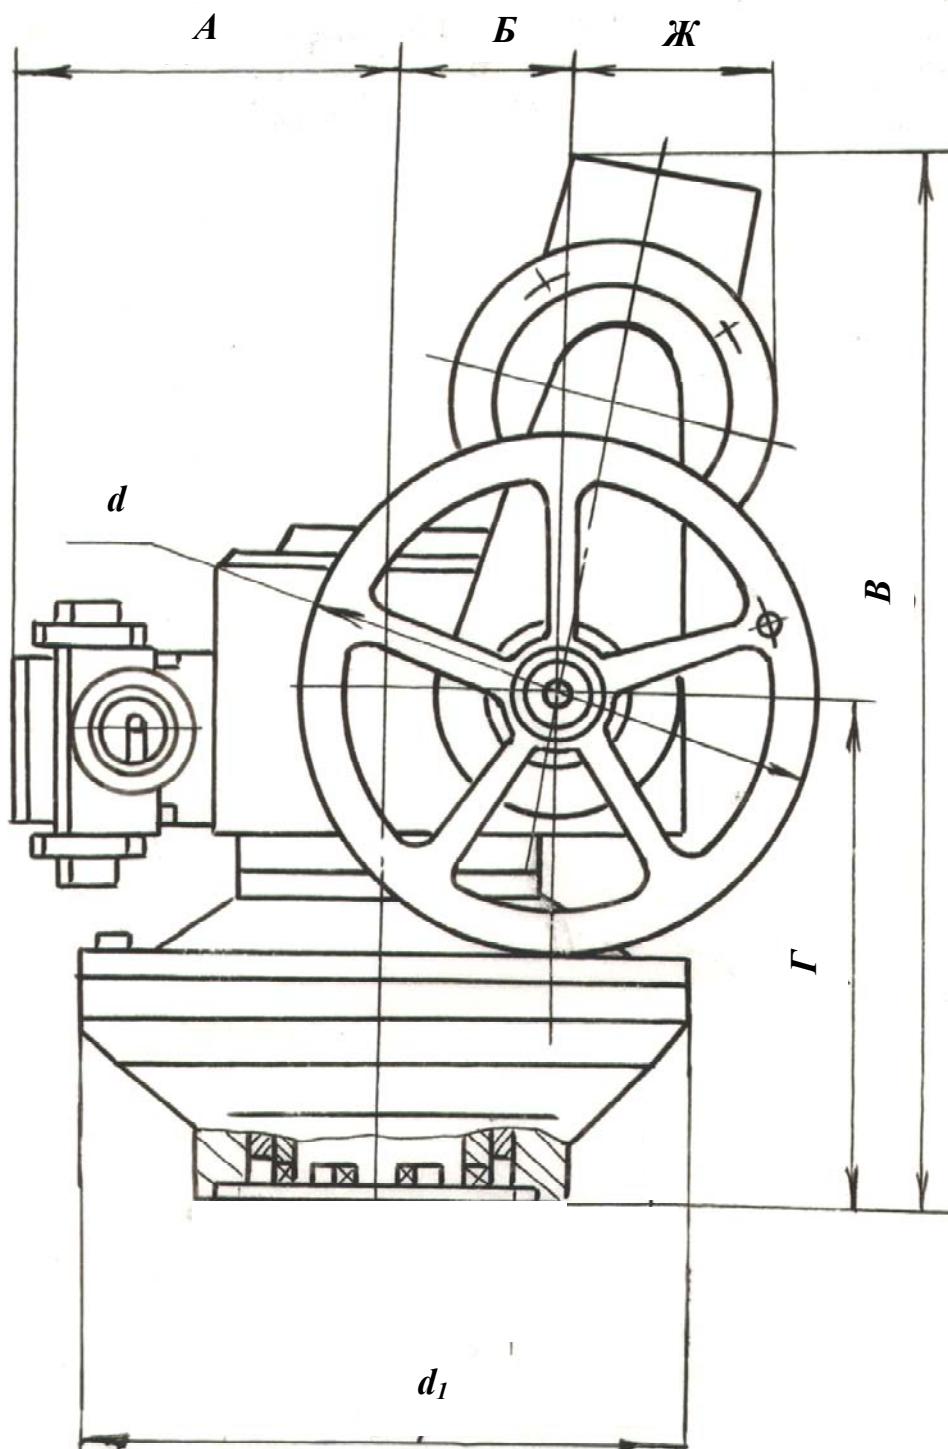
Общий вид и габаритные размеры электропривода типа Д
